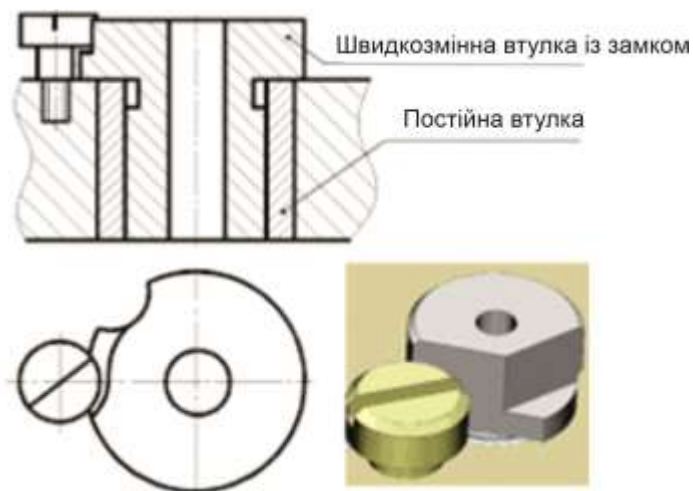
Схема розташування кондукторних втулок під час обробки кінцевим інструментом.
